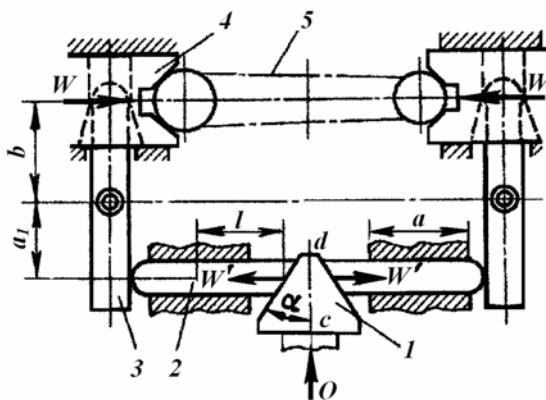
Схема комбинированного усилителя из клиноплунжерного и рычажного механизмов-усилителей для зажима детали
